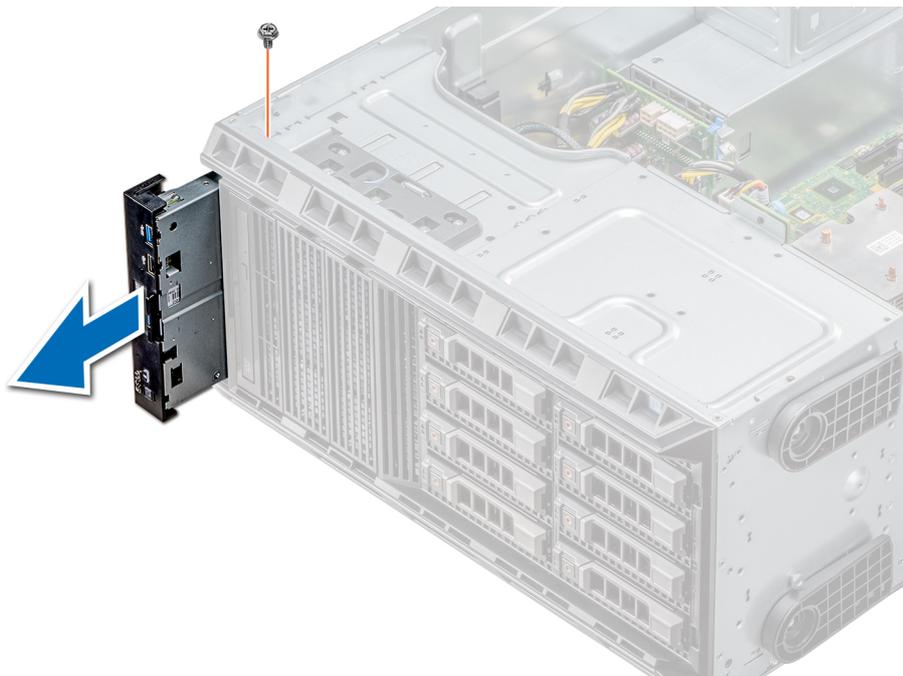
Entfernen der Bedienfeldbaugruppe
